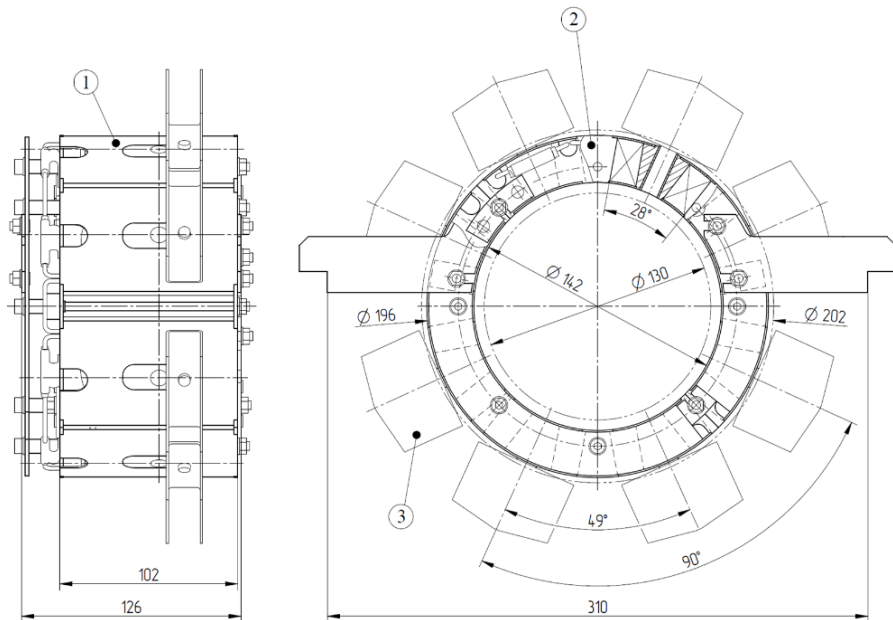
Конструкция дипольного корректора вставки транспортного канала (INSERT): 1) обмотка; 2) обечайки корпуса; 3) радиатор
